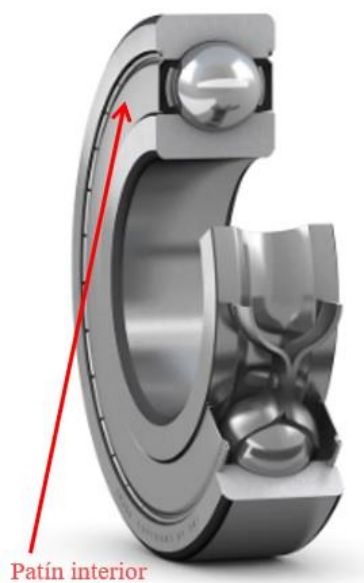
Vista detalle seccional del encaje del cojinete (Fuente 31)
